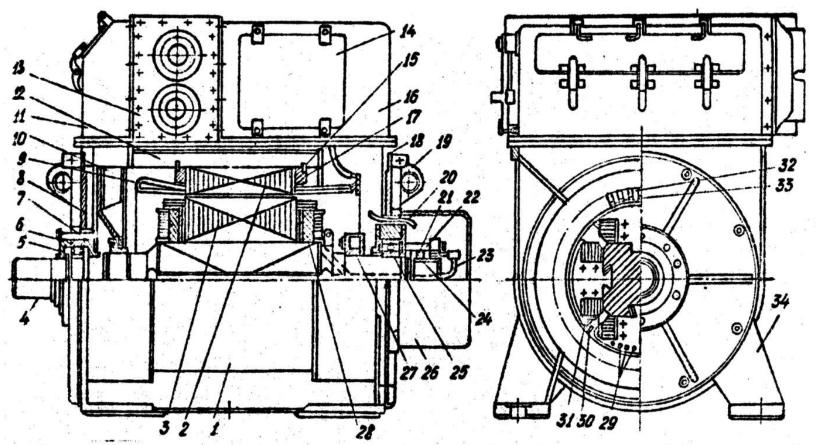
Устройство синхронного генератора серии МСК: I — станина; 2,3 — сердечник статора и польса рстора; 4 — вал; 5,7 — наружная и внутренняя крышки подшитника; 6,25 — роликовый и шариковый подшипники; 8,18 — задний и передний подшипниковые щиты; 9 — лобовые части обмотки статора; 10 — вентилятор; 11,16,26 — колпаки; 12 — опорные ребра; 13 — воздухоохладитель; 14 — локи; 15 — шпонка; 17 — щеки; 19 — рым; 20 — ка-бель для соепунения обмотки возбуждения с силовой системой возбуждения; 21 — контактные кольца; 22 — щеточное устройство; 23 — выводные концы обмотки возбуждения; 24 — втулка; 27 — балансировочная втулка; 28 — изоляция; 29 — демпферная обмотка; 30 — соединительные болты; 31 — катушка обмотки возбуждения; 32 — паз; 33 — клин; 34 — лачы
